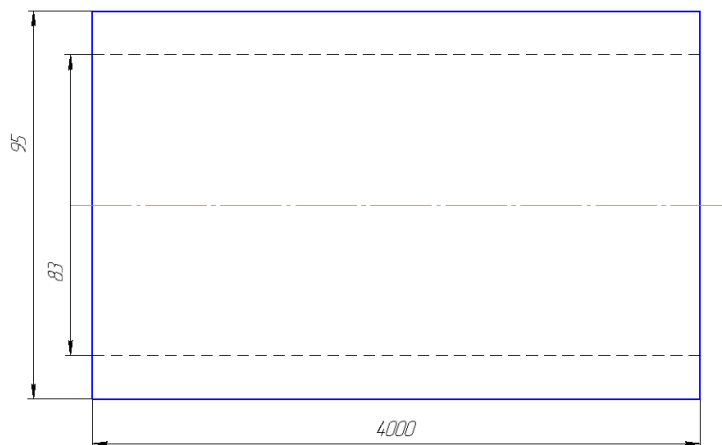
Ескіз заготовки з холоднодеформованого прокату
